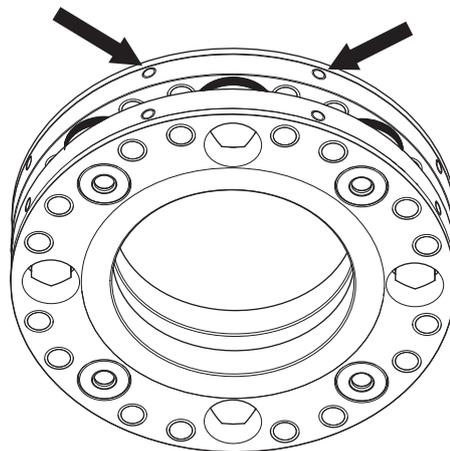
Gewindebohrungen für Transportvorrichtungen
